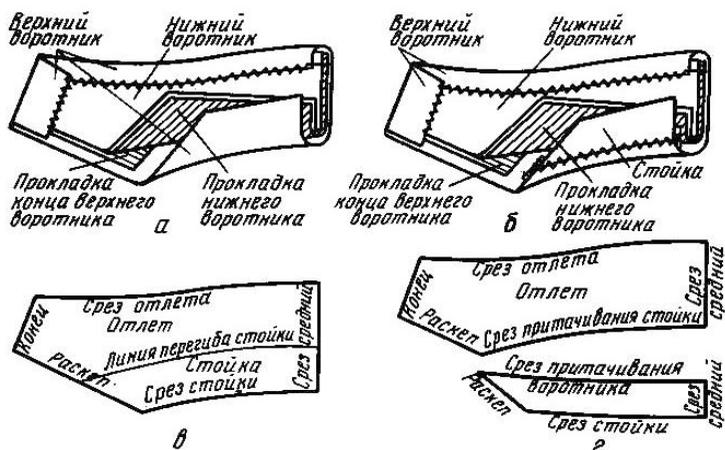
Конструкция узла и деталей воротника пиджака:
